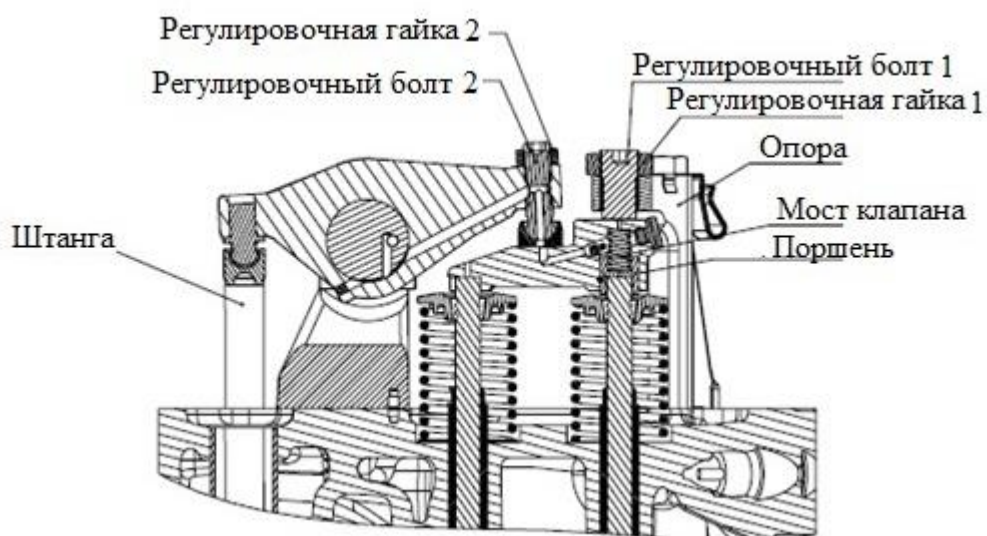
Регулировка зазора выпускного клапана с тормозным устройством WEVB
